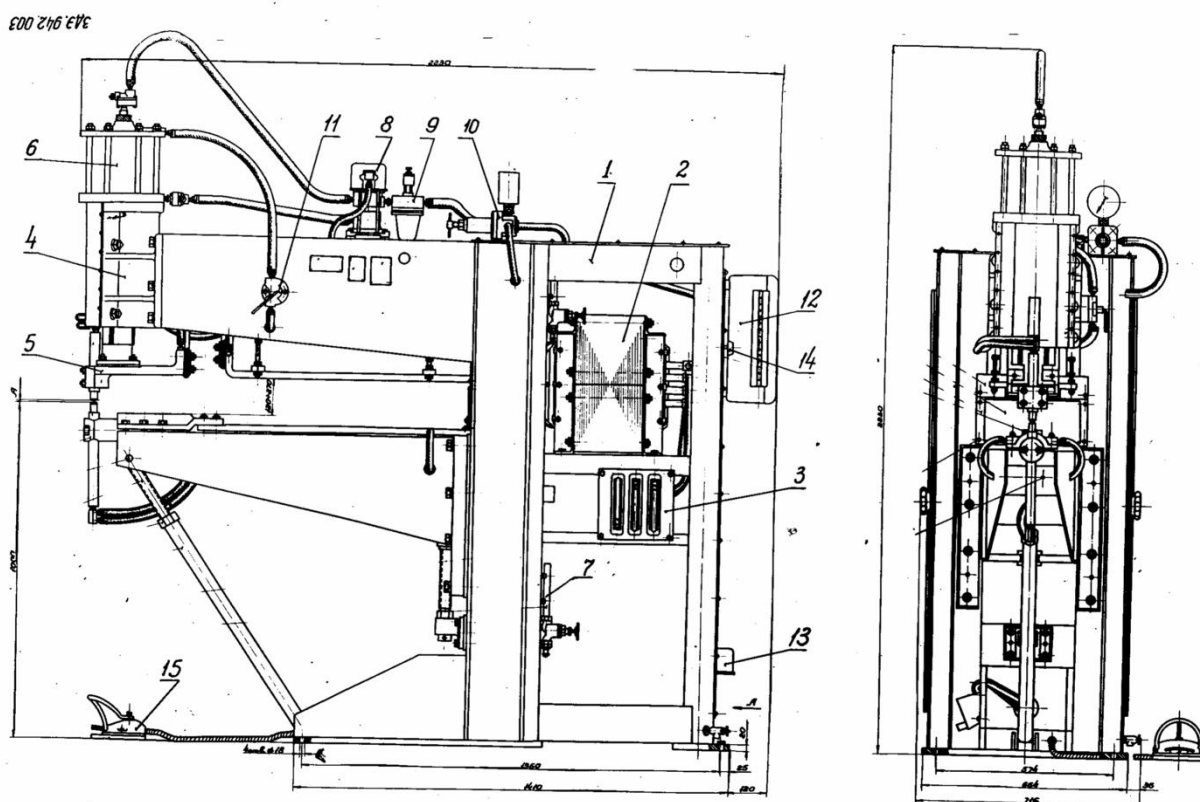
Конструкция машины для контактной сварки МТПУ-300
